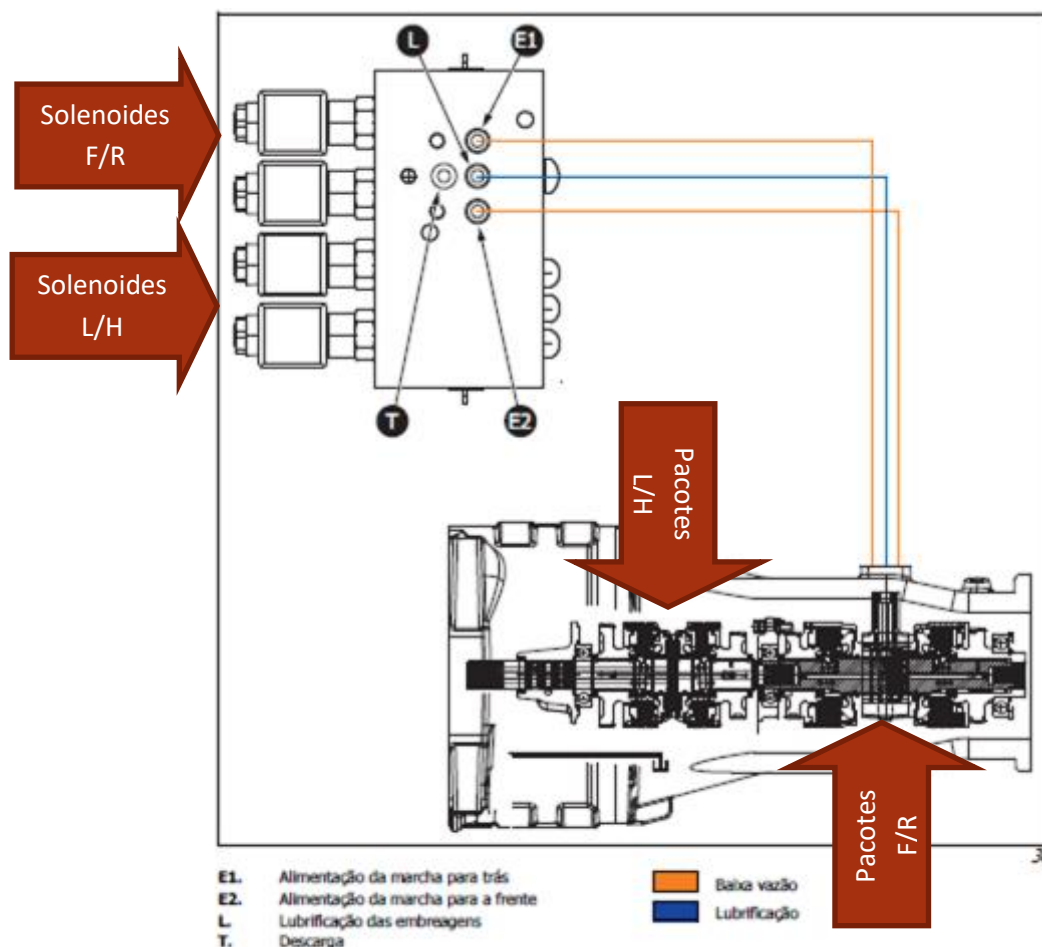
Vista explodida de 2 pacotes da embreagem hidráulica na transmissão
